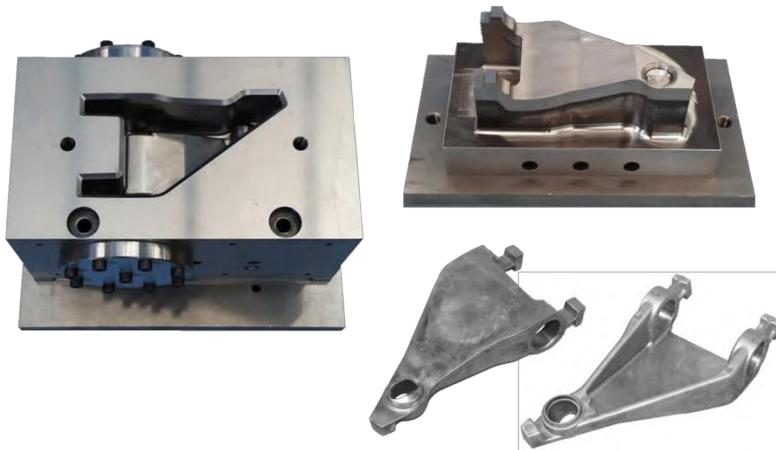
Werkzeug „Dreieckslenker“, Bauteile [14]
